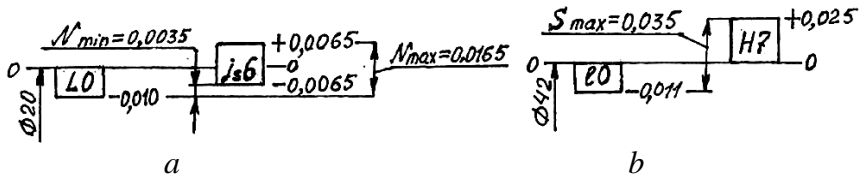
Схемы расположения полей допусков: *a* – посадка внутреннего кольца подшипника на вал $\Phi 20 L0 / i_6$ и *b* – посадка наружного кольца подшипника в корпус $\Phi 42 H7 / I0$.
